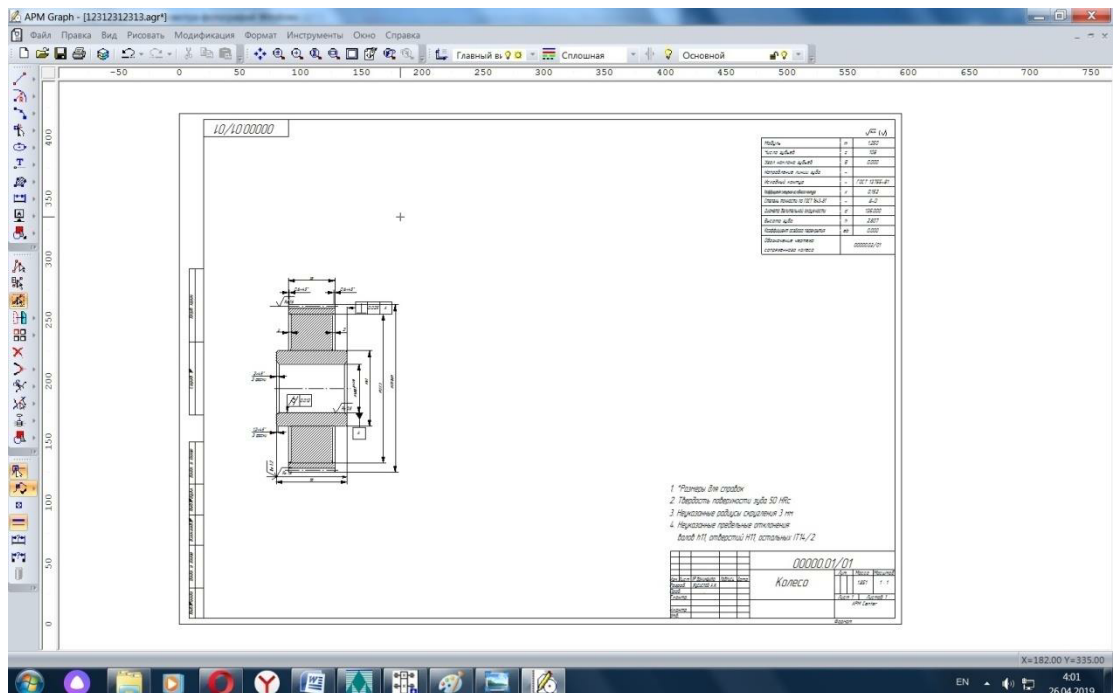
Готовая зарисовка чертёжа рассчитанного зубчатого колеса
